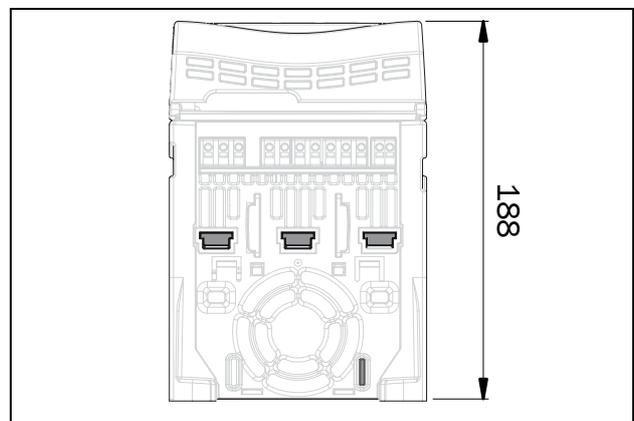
Габаритные размеры Emotron TSA типоразмеров 1 и 2, вид снизу.
